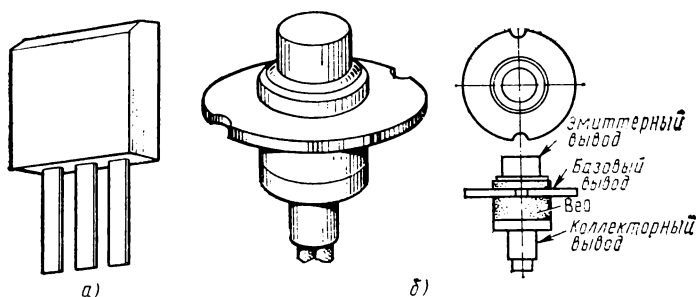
Пластмассовый корпус ВЧ-транзистора (а) и металлокерамический коаксиальный корпус СВЧ-транзистора (б)
